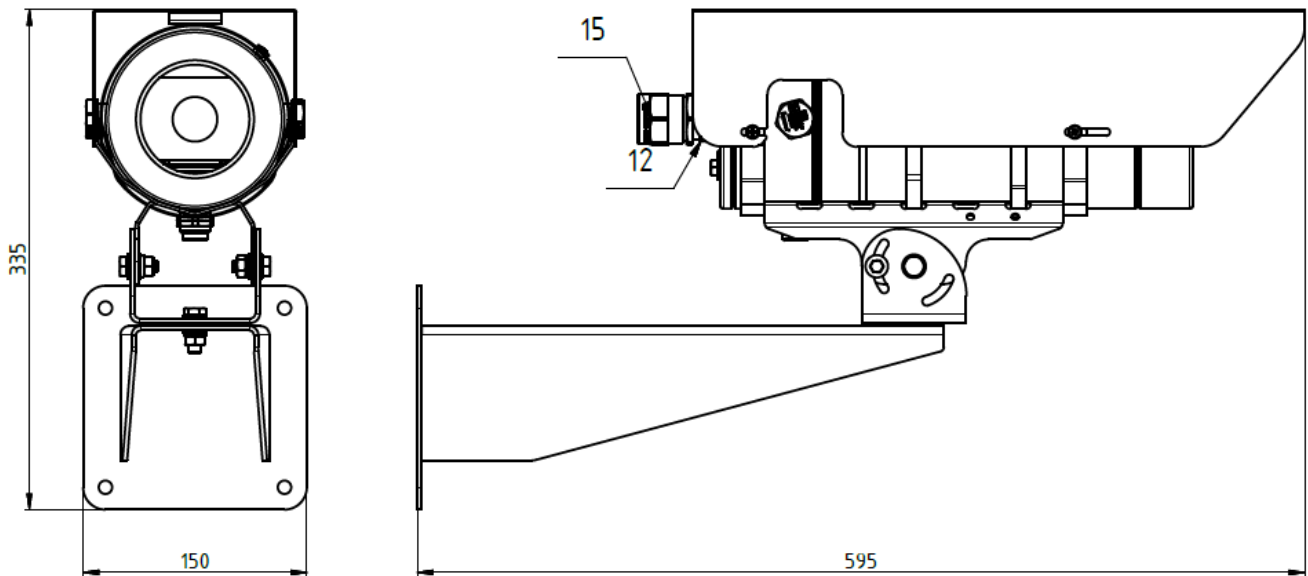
Габаритный чертеж видеокамеры ИВМ-501В.
